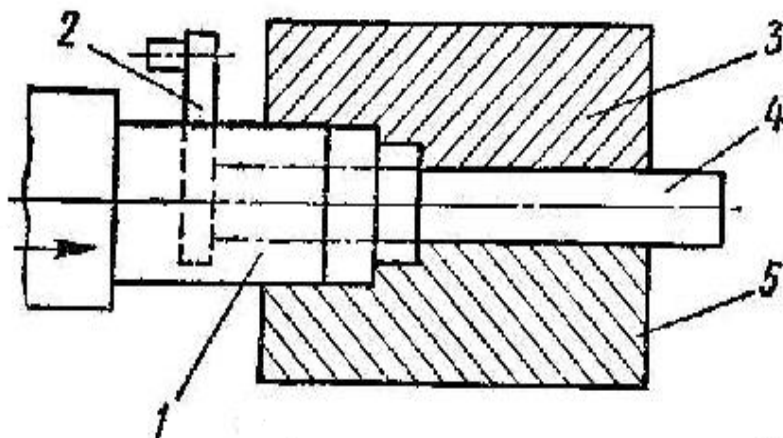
Схема штамповки ступенчатого вала с фланцем на ГКМ:
